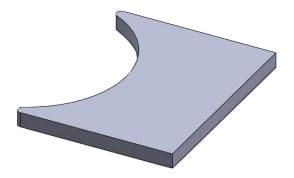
Detalle tope sistema empuñadura Fuente: Elaboración Propia
